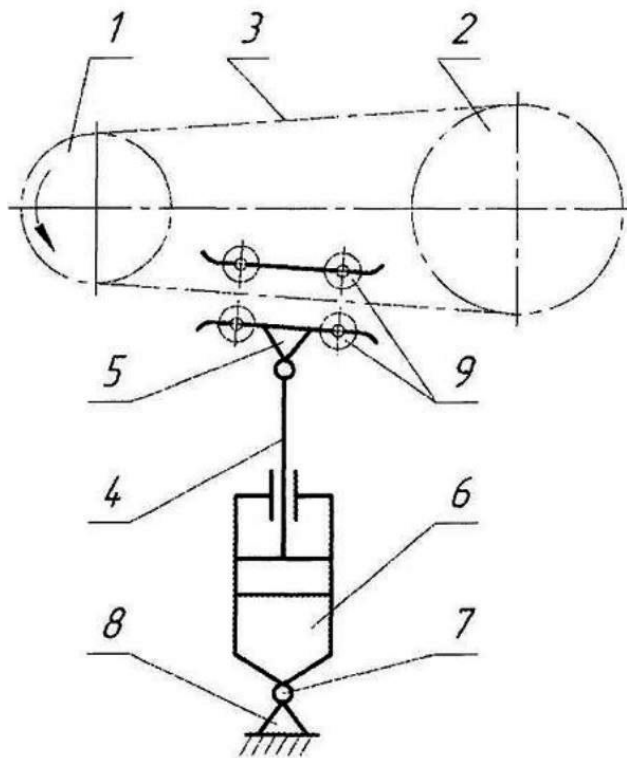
Кінематична схема ланцюгової передачі: 1 – ведуча зірочка; 2 – ведена зірочка, 3 – ланцюг; 4 – обмежувач коливань ланцюга; 5 – напрямні; 6 – демпфер; 7 – шарнір; 8 – нерухома опора
